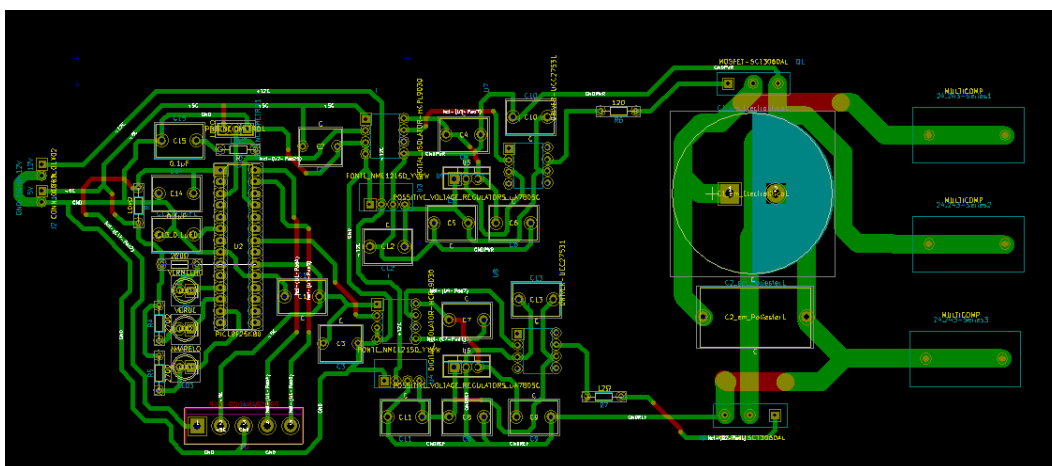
Esquema de pistas em placa de circuito impresso em Kicad
